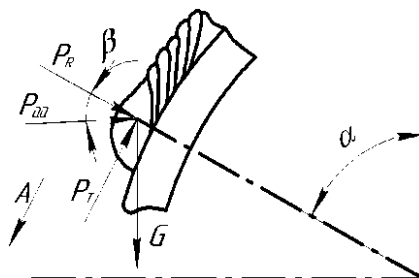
Схема сил действующих на сварочную ванну
